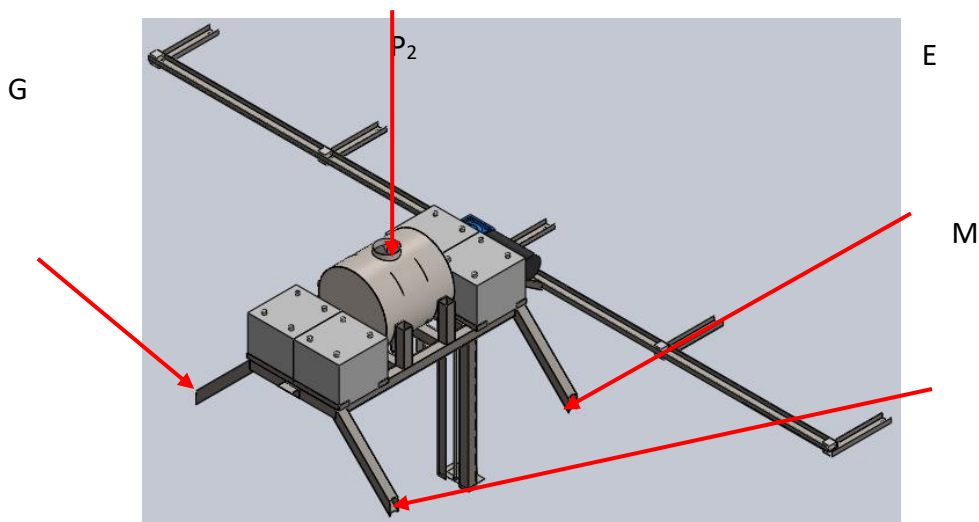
Ubicación de puntos de apoyo de la estructura de soporte del tanque, baterías y sistema de aspiración
